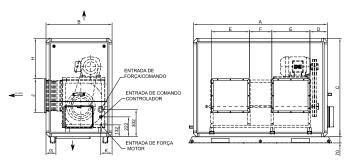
Cotas Módulo Ventilador WL02 a WL08 - Limit Load
